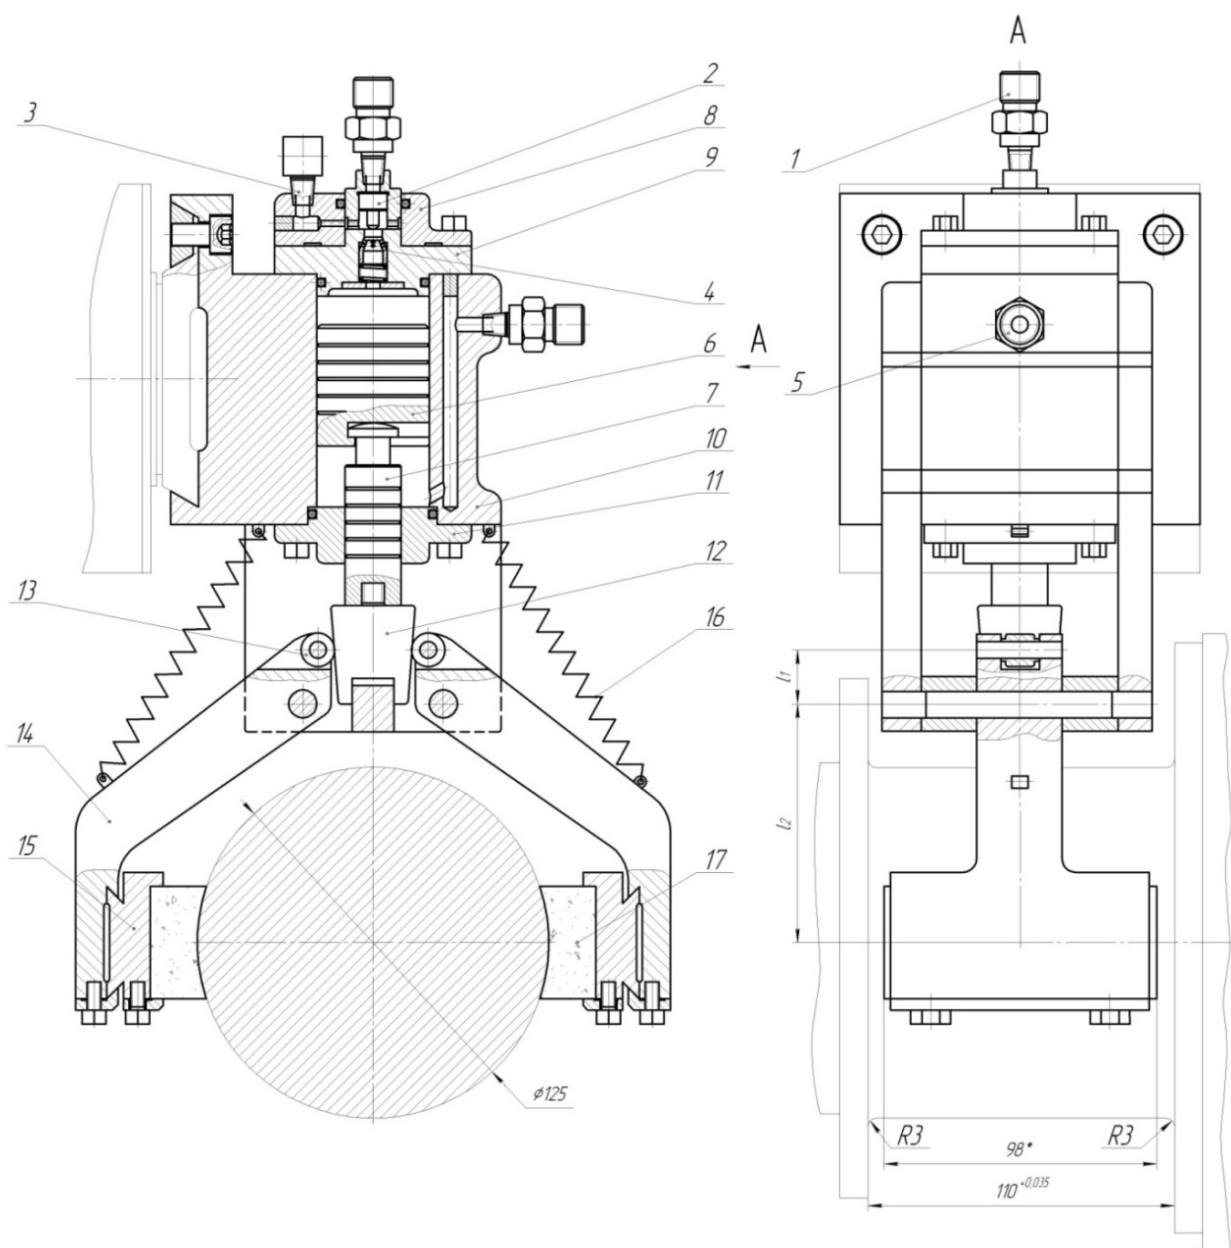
Інструментальна головка для суперфінішування шийок вала
